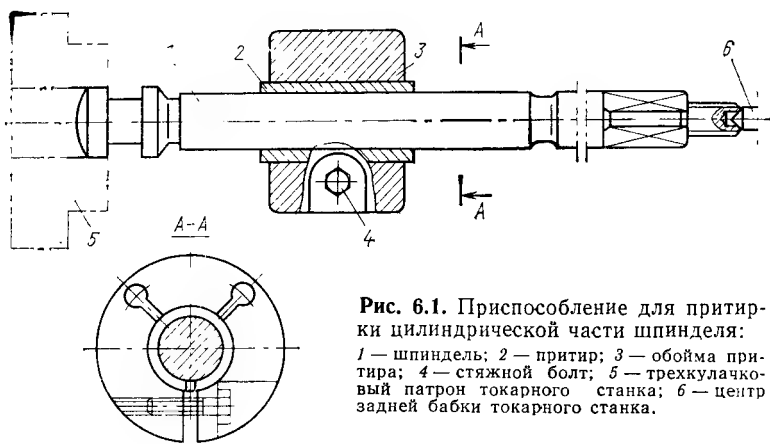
Приспособление для притирки цилиндрической части шпинделя:
